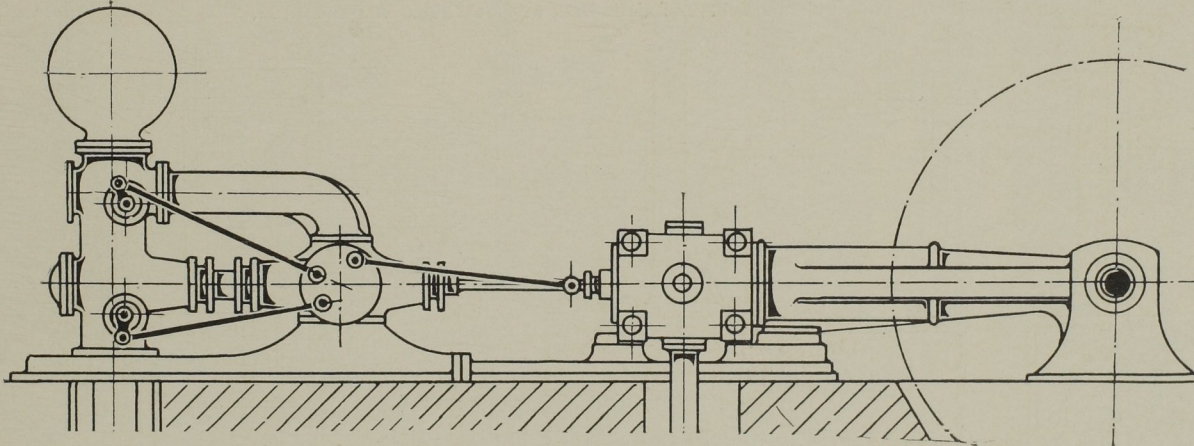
Seitenansicht der Maschine. Massst. 1:24.
